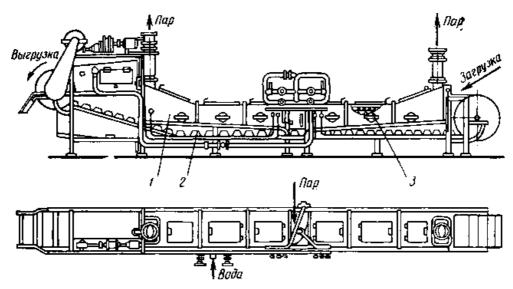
Ковшовий стрічковий бланшував марки БК: 1 – ванна; 2 – ковші; 3 – барботери
